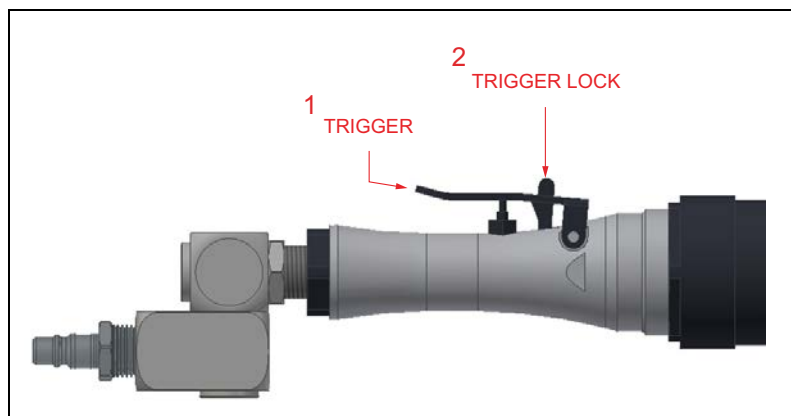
Включатель станка BF-R и блокиратор включателя
